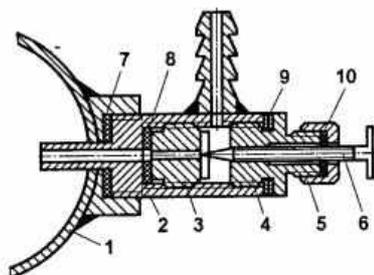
Схема безпоплавкового карбюратора для подачі води у впускний трубопровід дизеля Д-21А1 трактора Т-25А: 1 - впускний трубопровід; 2 – корпус; 3 - жиклер; 4 - корпус регулювальної голки; 5 - гайка сальника регулювальної голки; 6 - регулювальна голка; 7, 8, 9 - уплотнителіні прокладки; 10 - сальник регулювальної голки.
